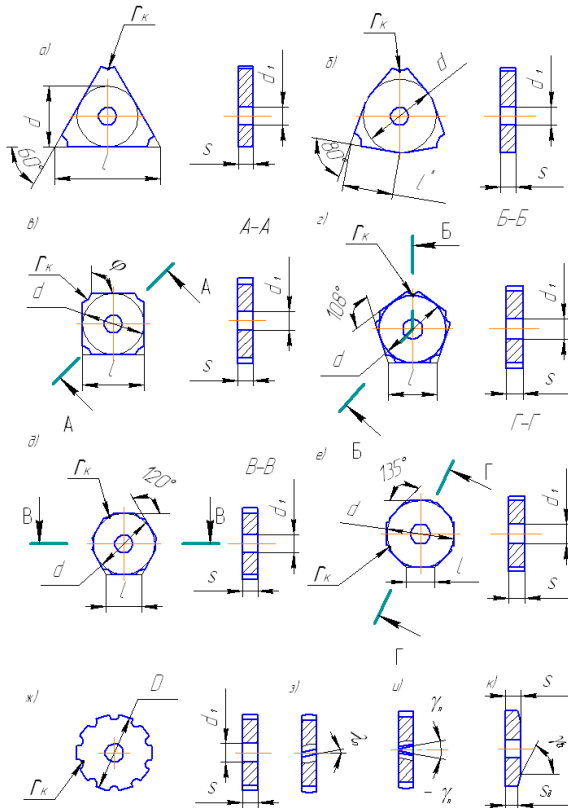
Предлагаемые МНП с выкружками – стружечными канавками
